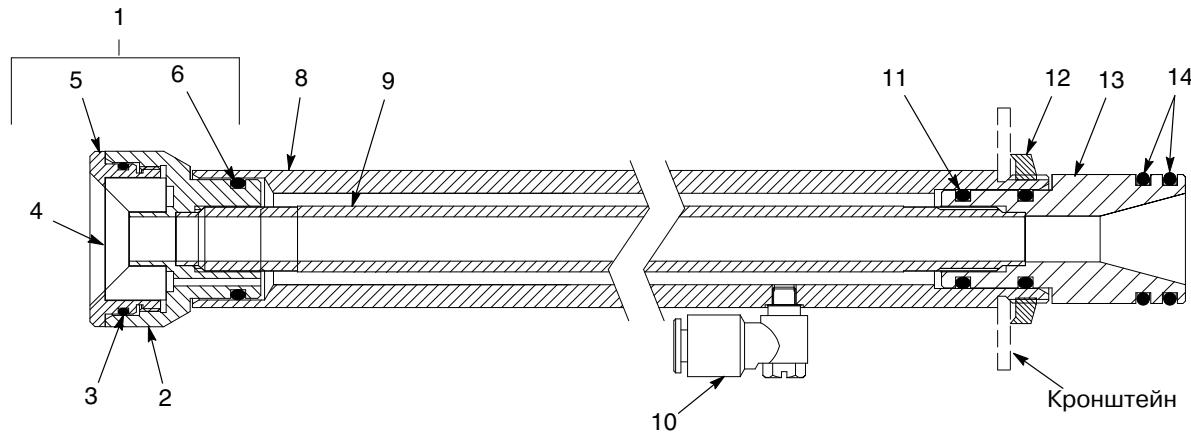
Детали резьбовой всасывающей трубы псевдоожижения
